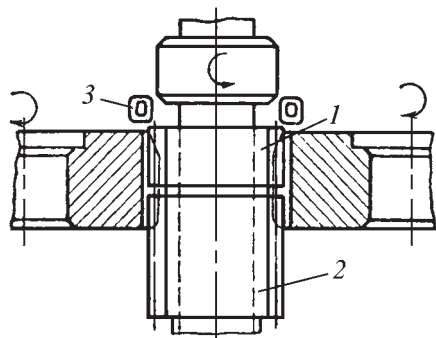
Схема накатывания шестерни с осевой подачей заготовки:
